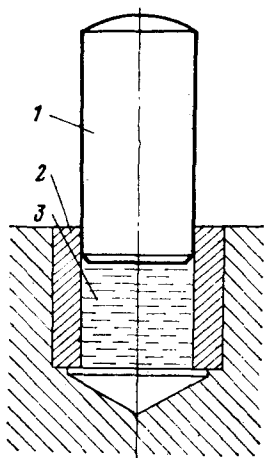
Гидравлический способ выпрессовки втулки из глухого отверстия:
